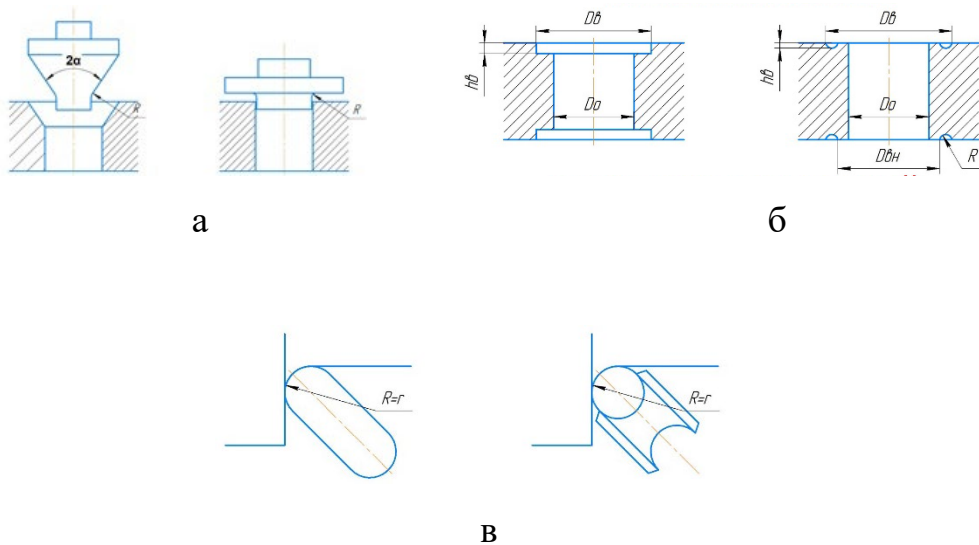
Обробка поверхонь переходу методами поверхнево-пластичного деформування: а – обробка динамічною чеканкою; б – обробка обтисканням; в – обробка роликками
